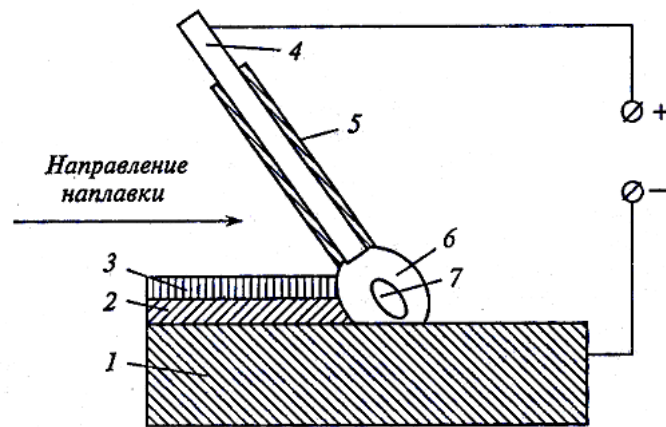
Схема ручной наплавки: 1 – основной металл; 2 – наплавленный валик; 3 – шлаковая корка; 4 – электродный стержень; 5 – покрытие электродного стержня; 6 – газшлаковая защита; 7 – сварочная ванна
